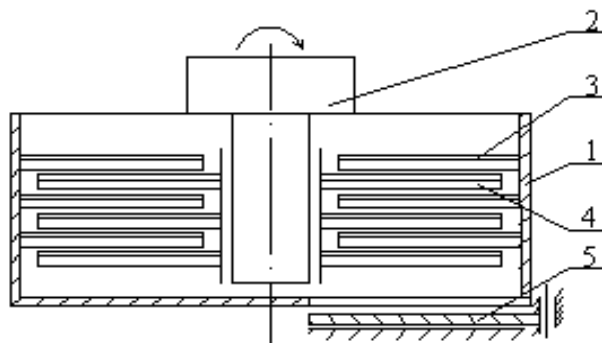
Бетоносмеситель с новым рабочим органом: 1 — корпус; 2 — ротор; 3 — подвижные лопасти; 4 — неподвижные лопасти; 5 — затвор
